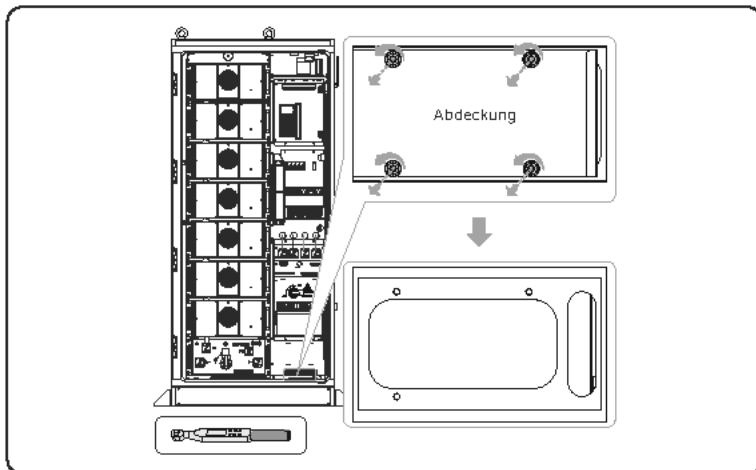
M4-Schrauben abschrauben und Abdeckung entfernen
